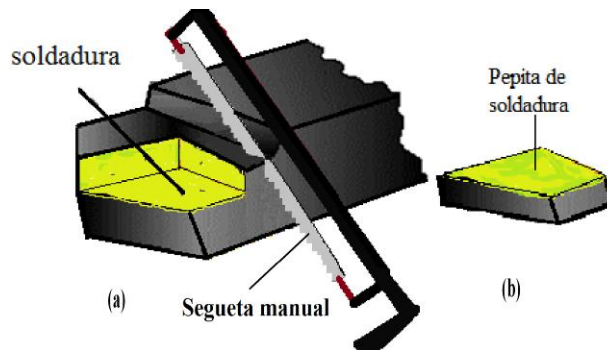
(a). Corte horizontal de la soldadura. 2.5 (b). Pepita de soldadura.
